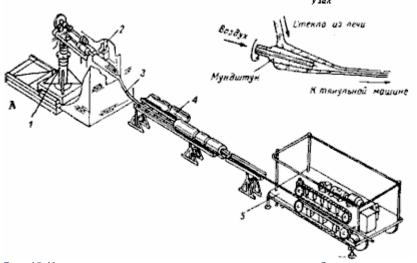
Установка для горизонтального вытягивания трубок: /—мундштучная машина; 2 — шибер, регулирующий подачу стекла; 3— трубка; 4~отжигательный канал. 5—цепная тянульная машина.
